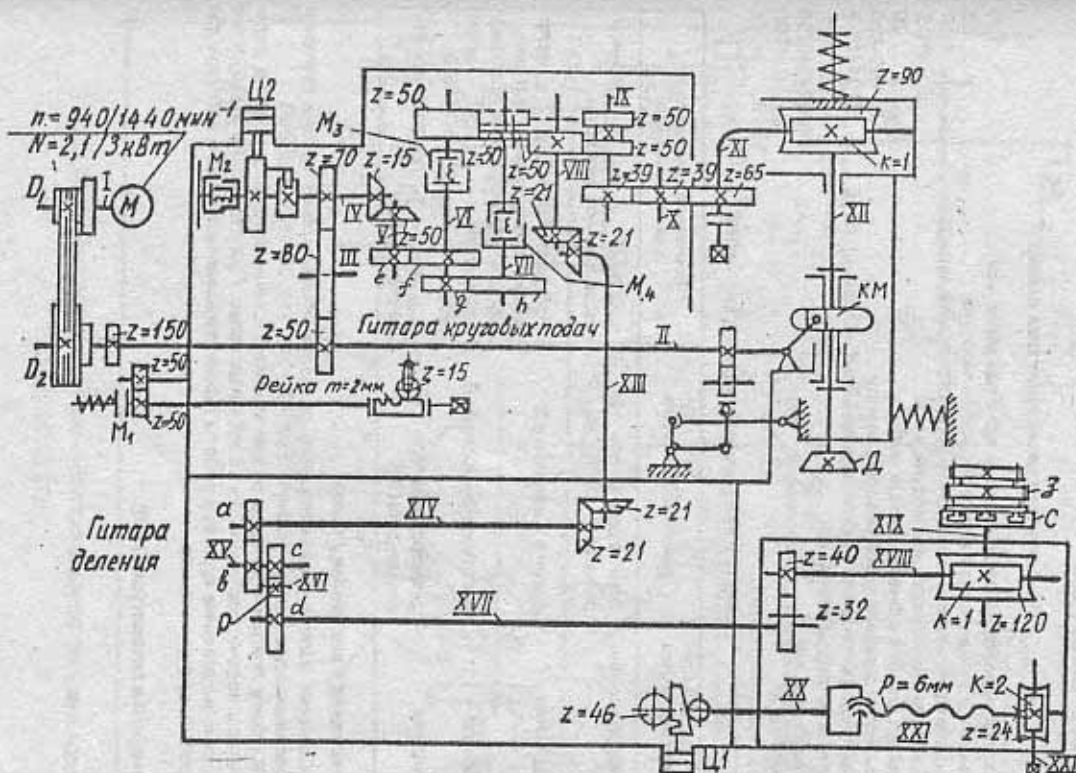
Кинематическая схема зубодолбежного станка мод. 5122
